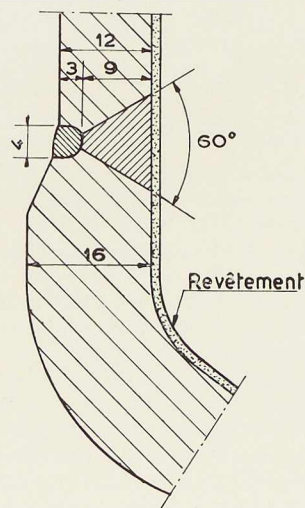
Assemblage du fond bombé sur la virole. Section du cordon de soudure et du cordon de reprise.
